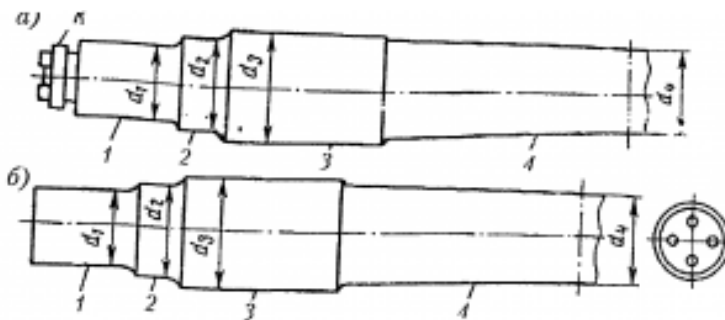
Осі колісних пар: а — РУ1; б — РУ1Ш; К — нарізна частина осі; 1 — шийка; 2 — передпідматочинна частина; 3 — підматочинна частина осі; 4 — середня частина осі;  $d_1$  — діаметр шийки;  $d_2$  — діаметр передпідматочинної частини;  $d_3$  — діаметр підматочинної частини;  $d_4$  — діаметр середньої частини.
